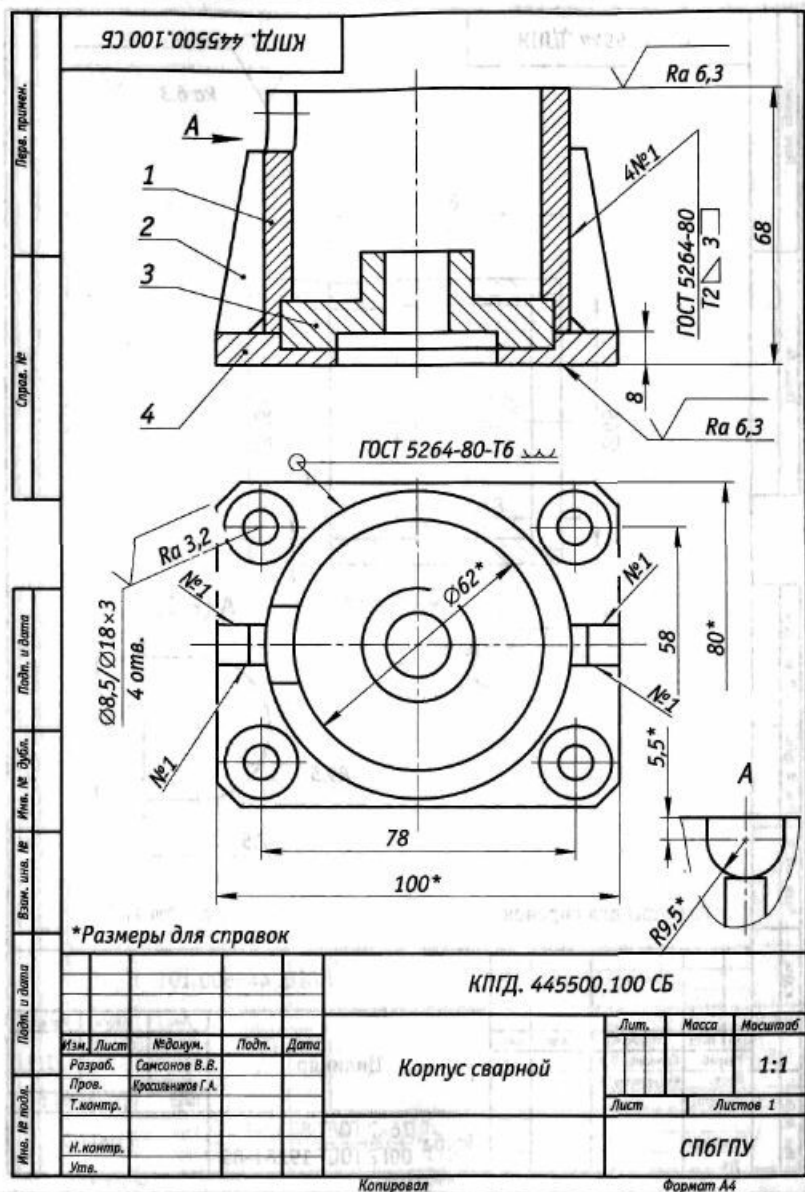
Сборочный чертеж корпуса «Амортизатор 1»
